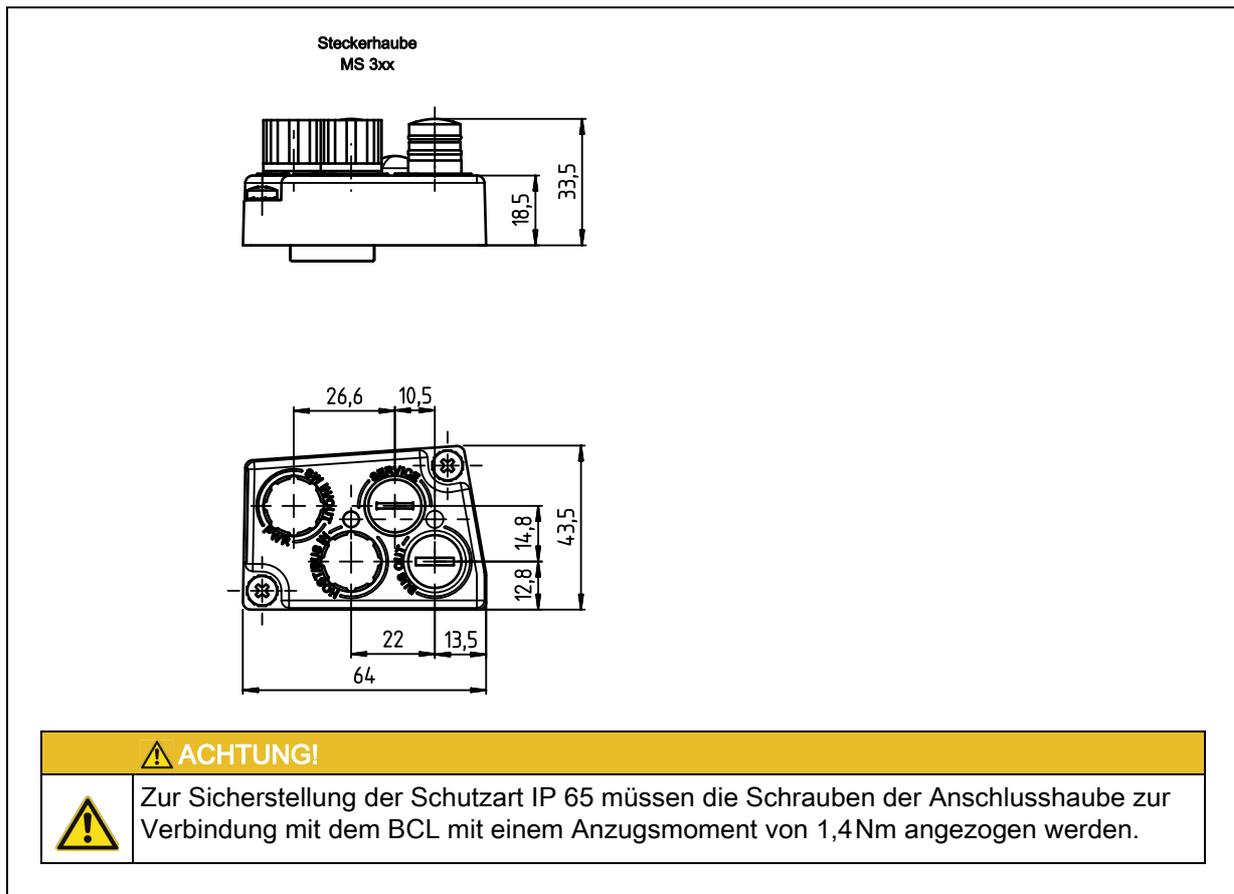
Maßzeichnung Steckerhaube MS 3xx
